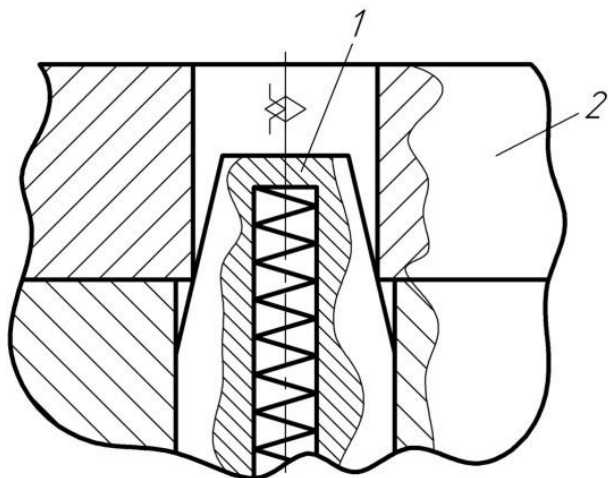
Установка заготовки с помощью конического пальца
